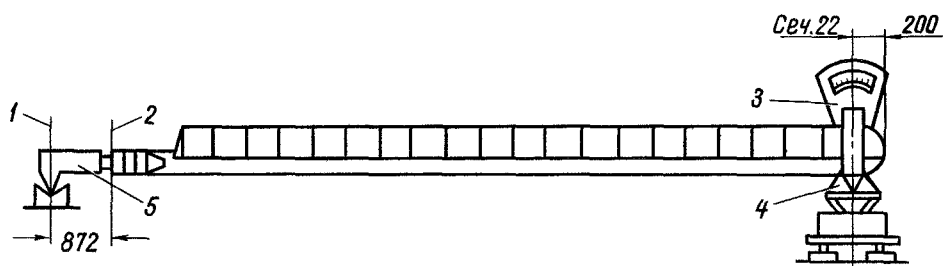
Установка лопасти несущего винта с приспособлениями на весы:
